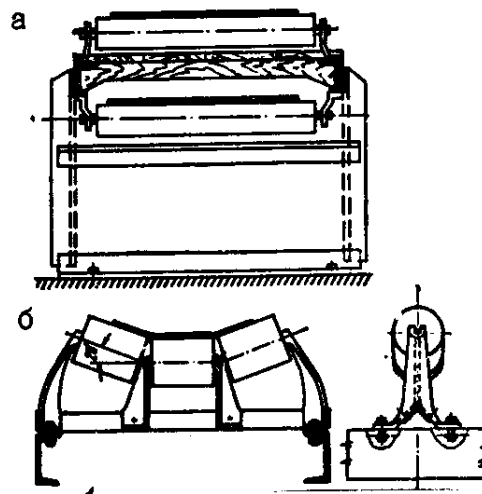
Роликоопори: а) – однороликова; б) – багатороликова
